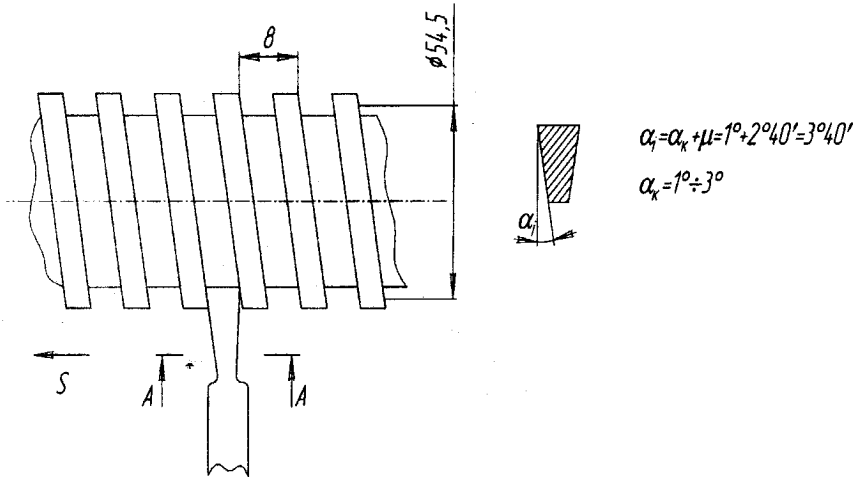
Ходовий гвинт і різець для його обробки
